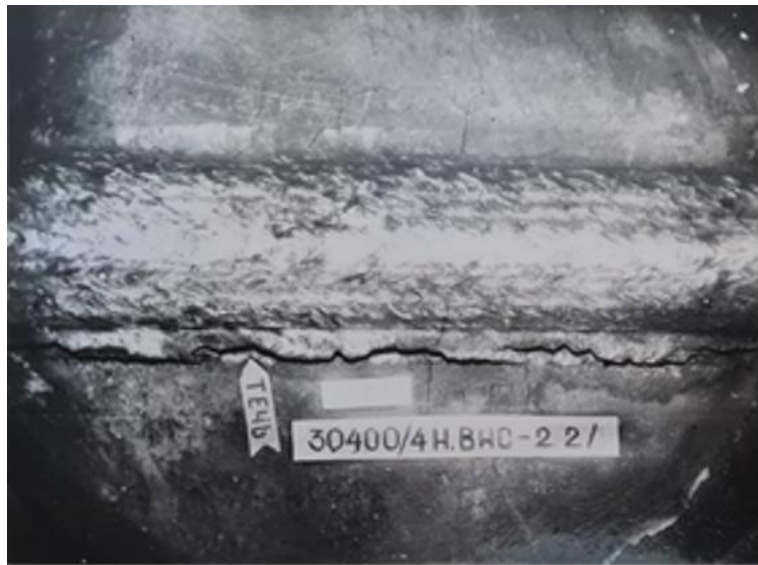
Разрушение стыкового сварного соединения, выполненного 5-м способом (фото авторов)
